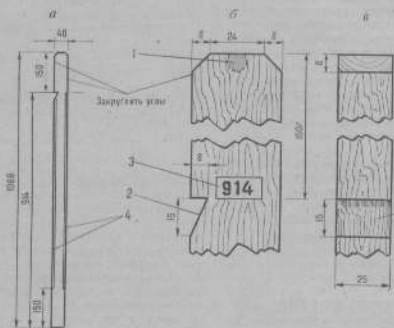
Подпорка для сетки: а — общий вид подпорки с широкой стороны; б — деталь подпорки; в — вид подпорки с узкой стороны. Обозначенные цифрами: 1 — желобок для троса; 2 — вырез для замера высоты середины сетки; 3 — цифра «914» в прямоугольнике; 4 — фаска
